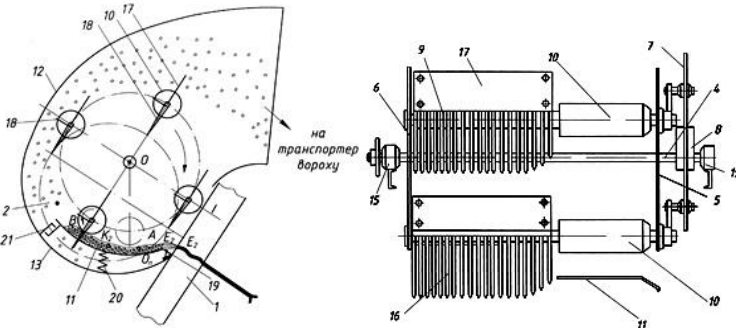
Плющильно-обчисувальний апарат: 1 – затискний транспортер; 2 – обчисувальна камера; 3 – барабан; 4 – вал; 5, 6, 7 – диски; 8 – ексцентриковий механізм; 9 – гребені; 10 – плющильні вальці; 11 – опорна направляюча поверхня; 12 – корпус; 13 – піддон; 14, 15 – підшипники; 16 – обчисувальні зуби; 17, 18 – лопаті; 19 – куліса; 20 – пружина; 21 – упор
